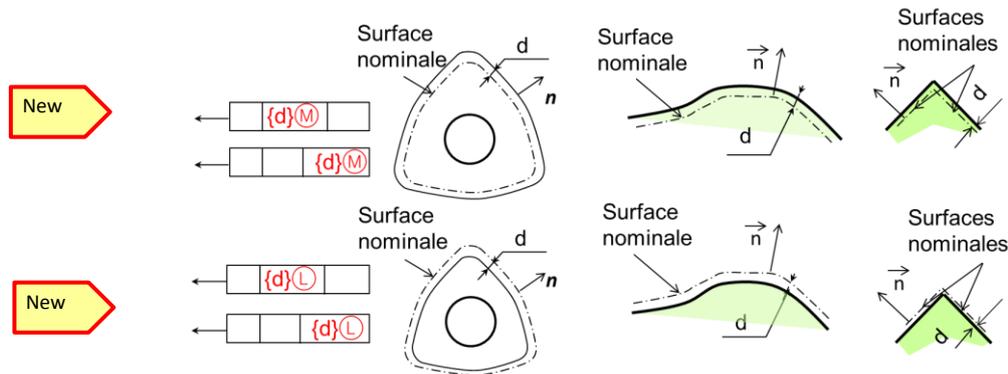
Zone de tolérance au maxi/mini matière sur une surface
